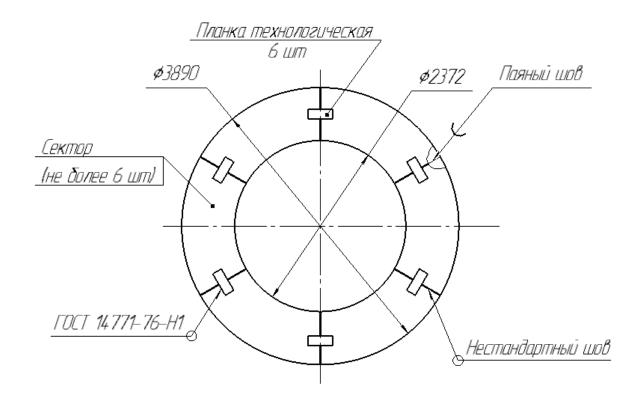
Проектный чертёж для сборки диска мельницы-вентилятора, швы паянные.
